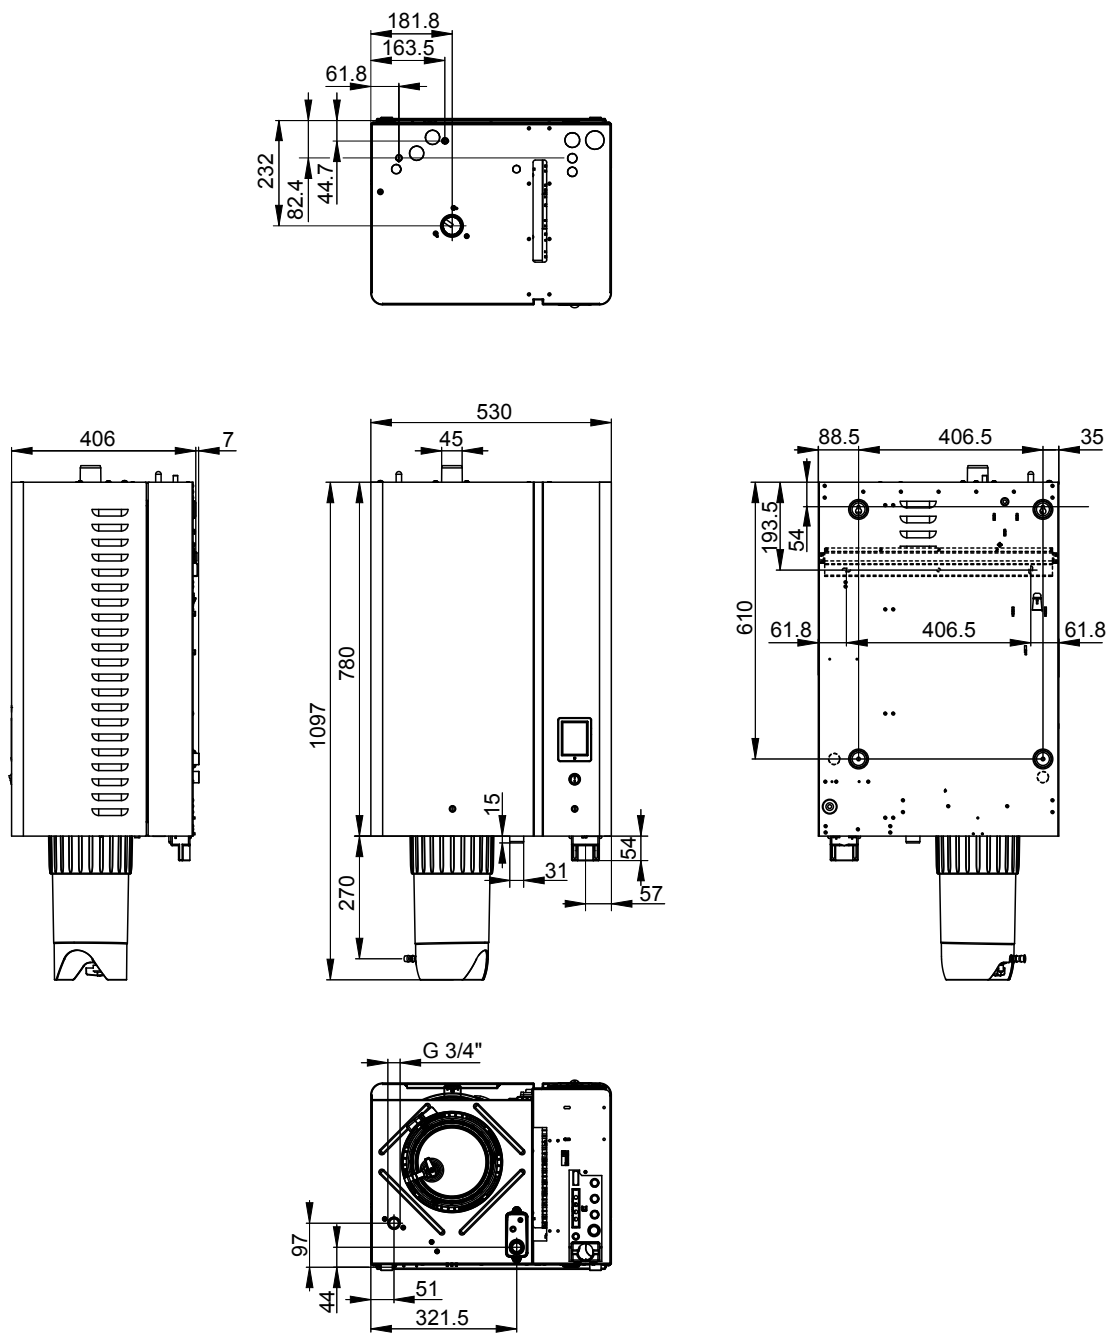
Чертеж с размерами устройства "М" (размеры в мм)
